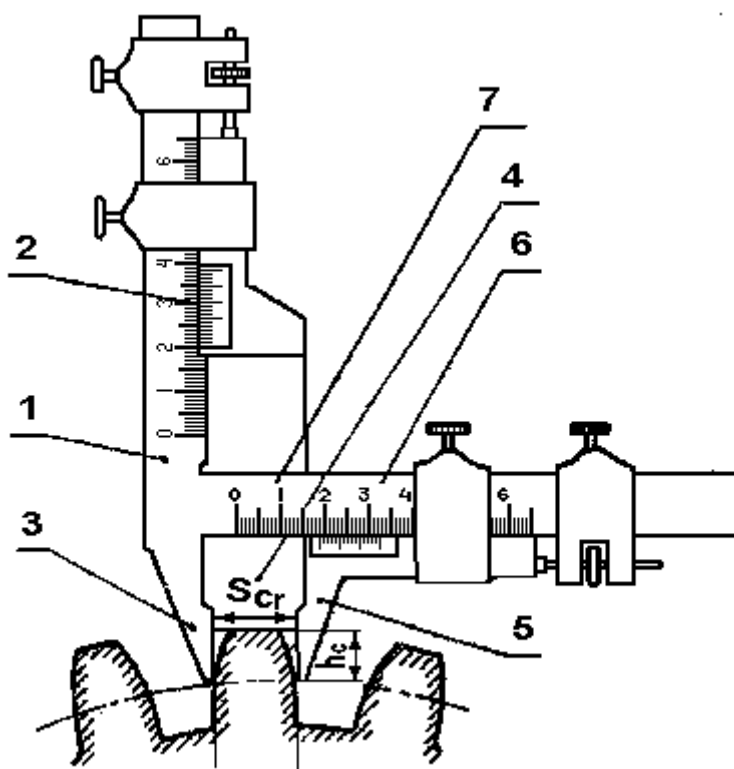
Схема вимірювання товщини зуба по сталій хорді штангензубоміром
